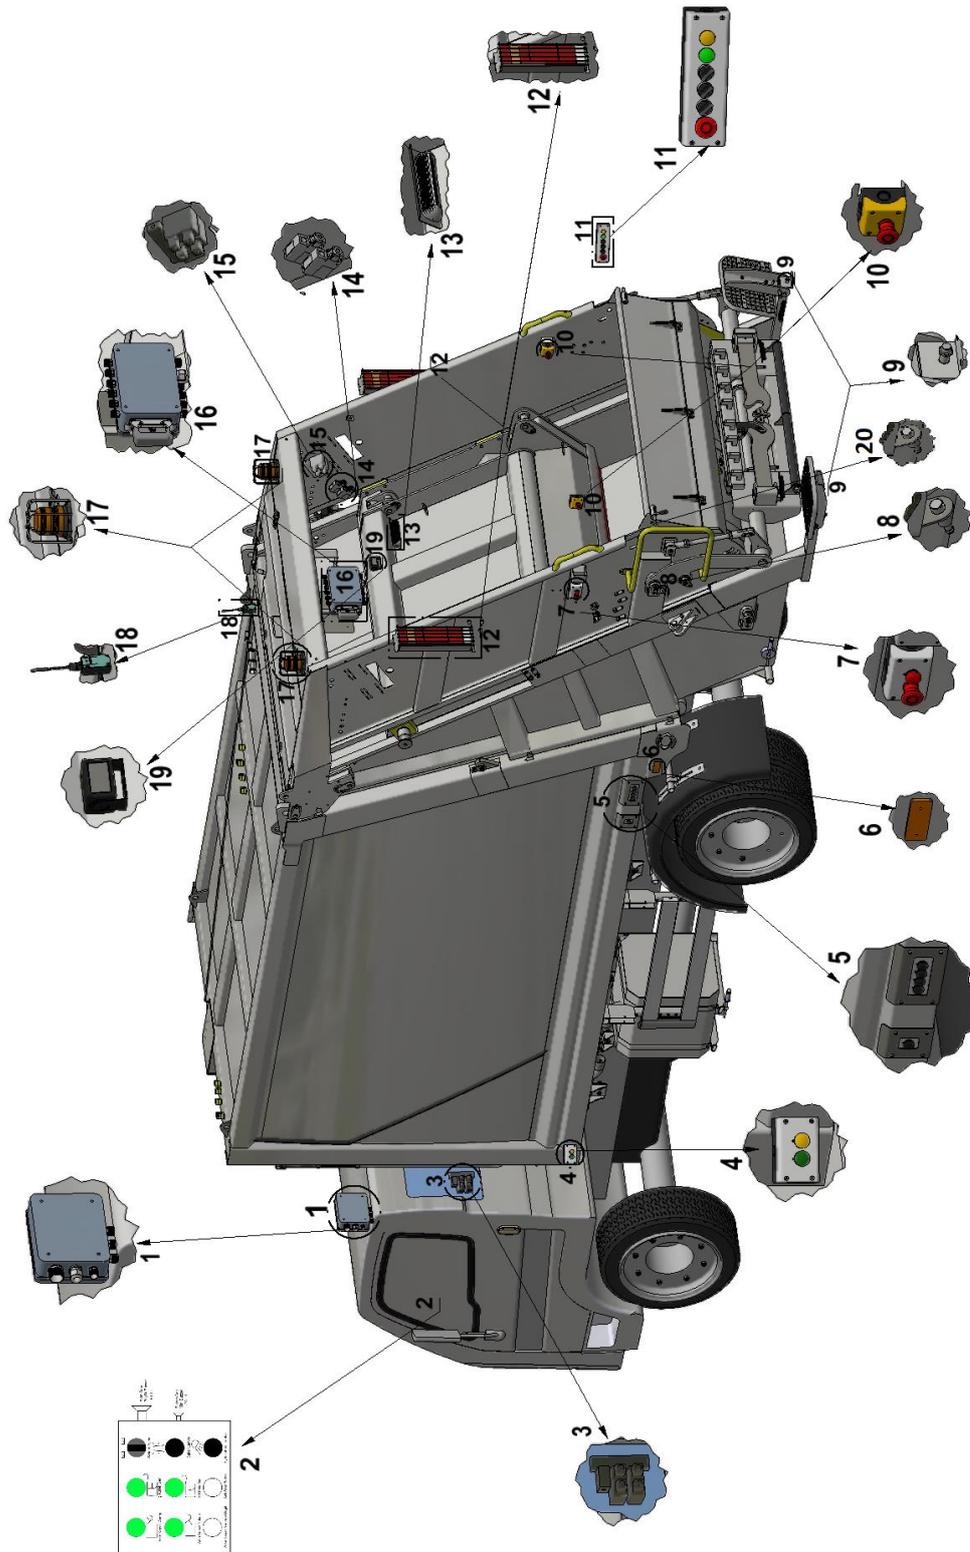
Los Montajes de Piezas Eléctricas del Equipo.
